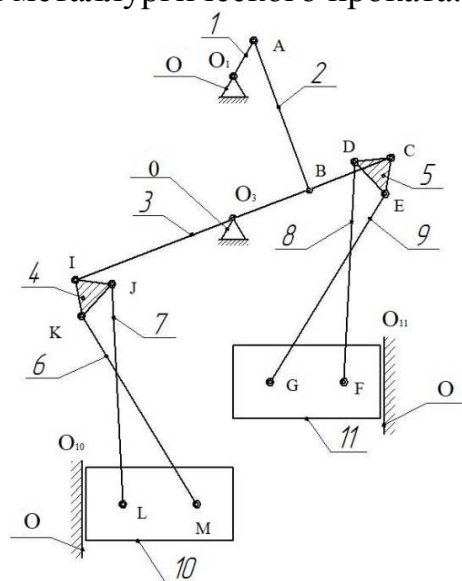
Ножницы с параллельными ножами с четырьмя тягами по [2, 3]
